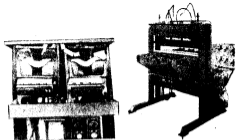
Станок для предварительной прессовки заготовки молоточкового войлока
